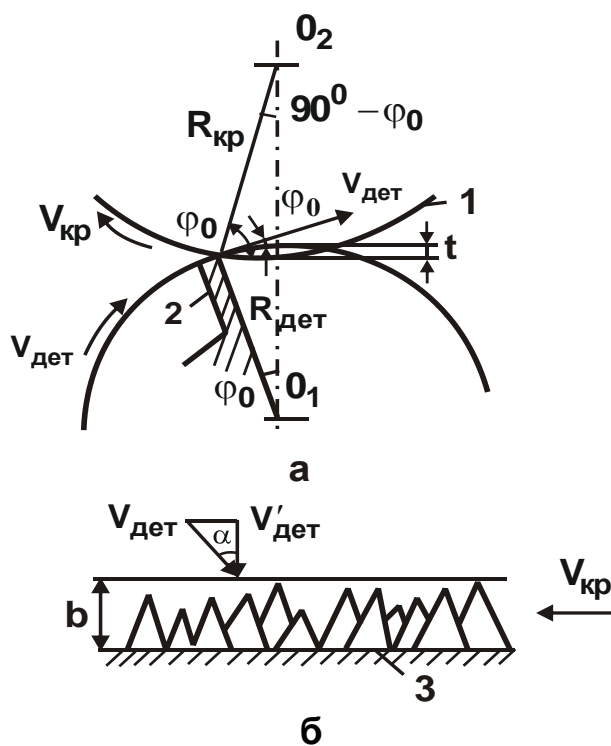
Розрахункова схема круглого поздовжнього шліфування:
